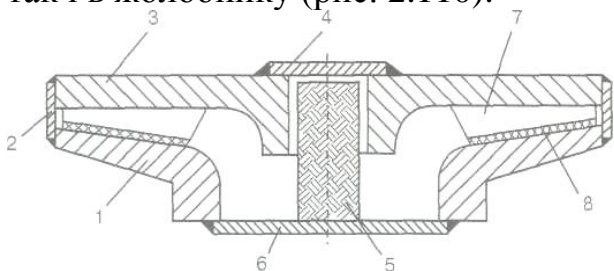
Схема автовакуумного паяння робочого колеса:
